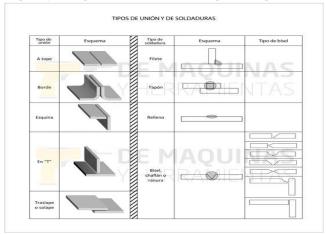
Uniones más comunes que se pueden soldar con el proceso MIG/MAG.
